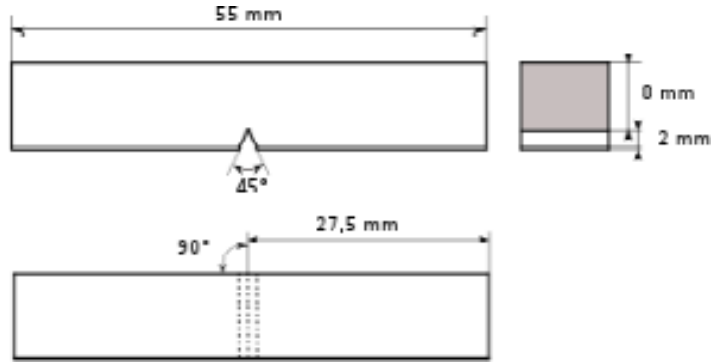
forme et dimension de l'éprouvette de résilience [2]
